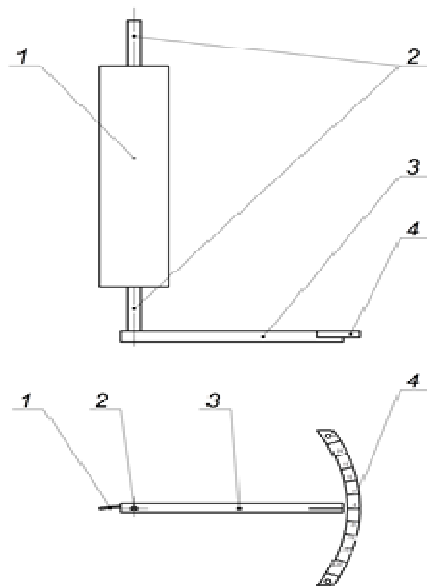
Схема конструктивна механізму керування направляючих лопаток: 1 – направляюча лопатка; 2 – консоль; 3 – важіль; 4 – сектор керування
